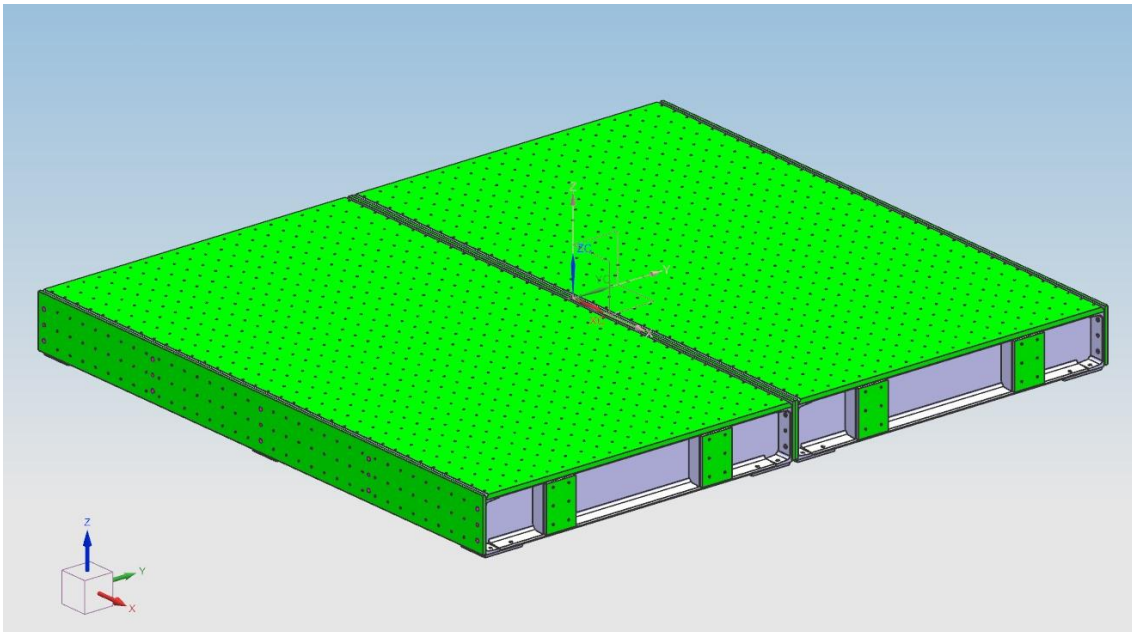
Mármol para el útil de montaje de cabina Eurodual con código
